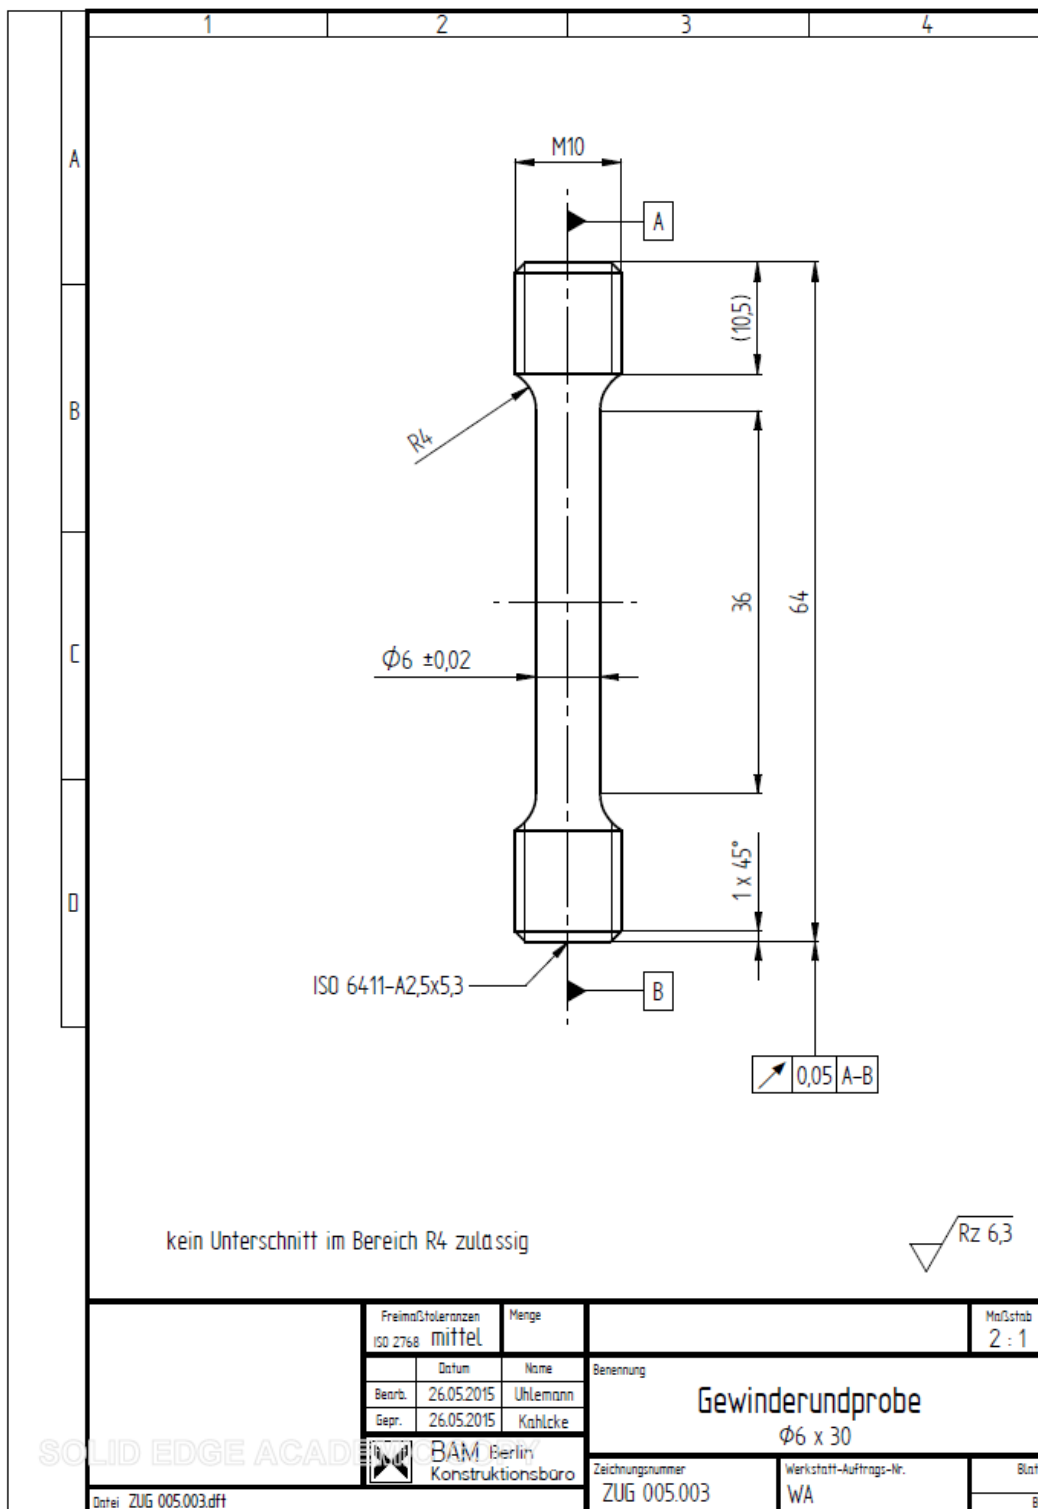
Technische Zeichnung Zugproben B 6 × 36 gemäß DIN 50125 [191].
